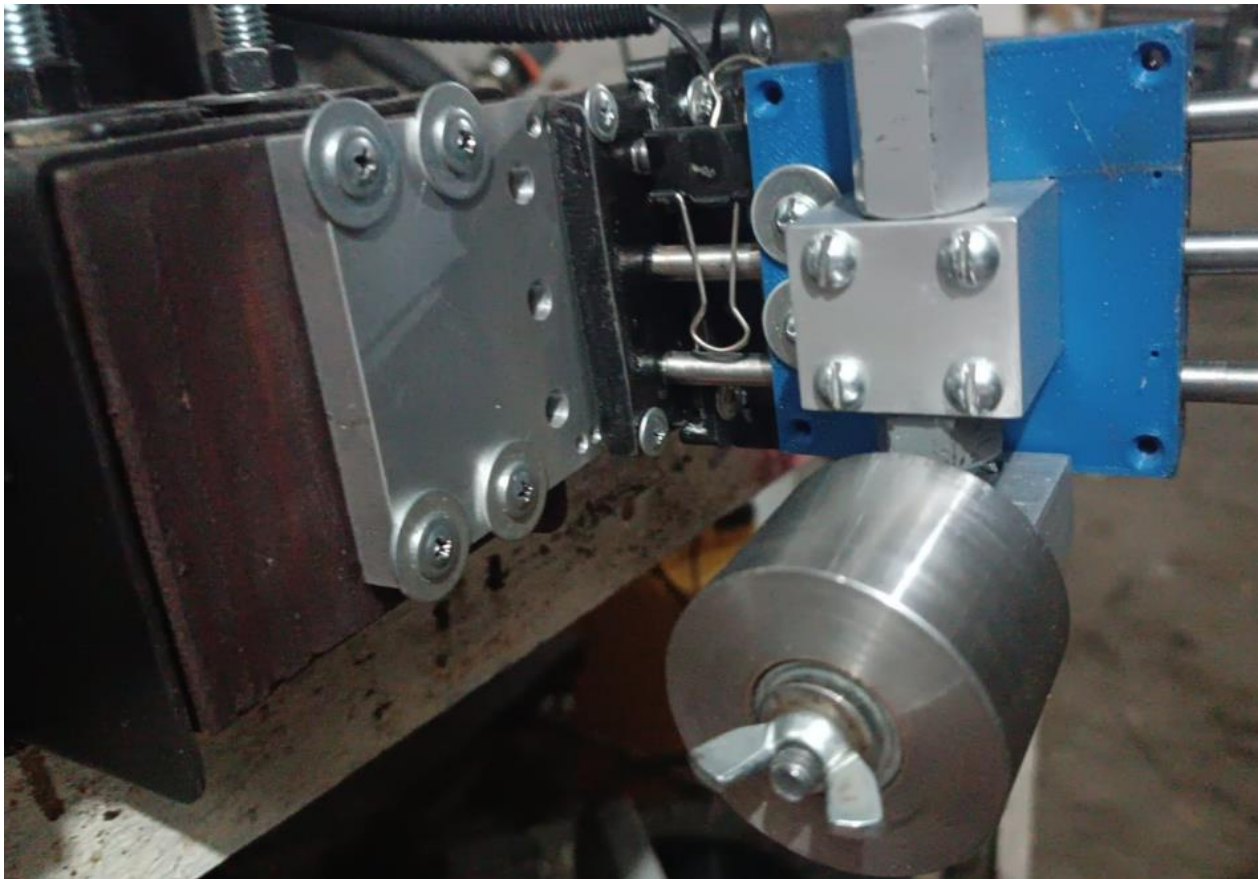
Dispositivo E.M.G. con piezas manufacturadas ya ensambladas.
